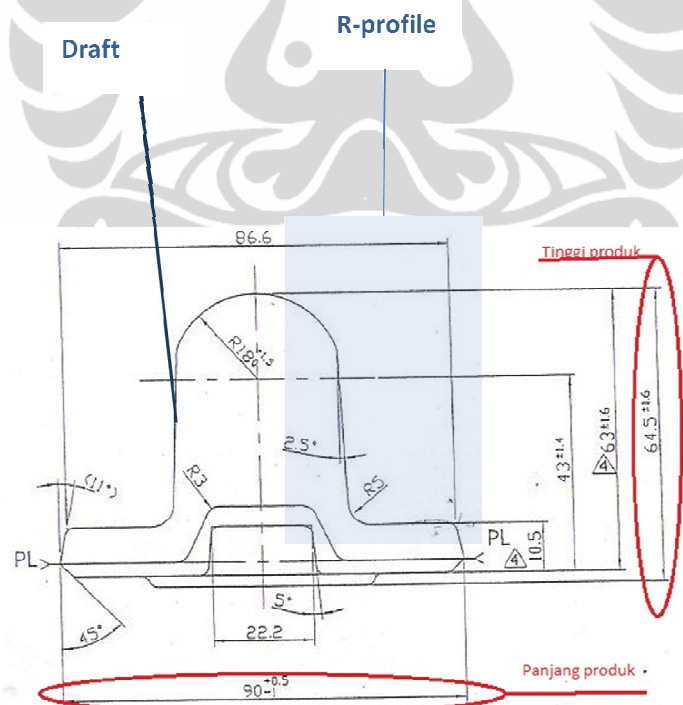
1 Komponen Propeller Shaft (Sumber: PT.X)
